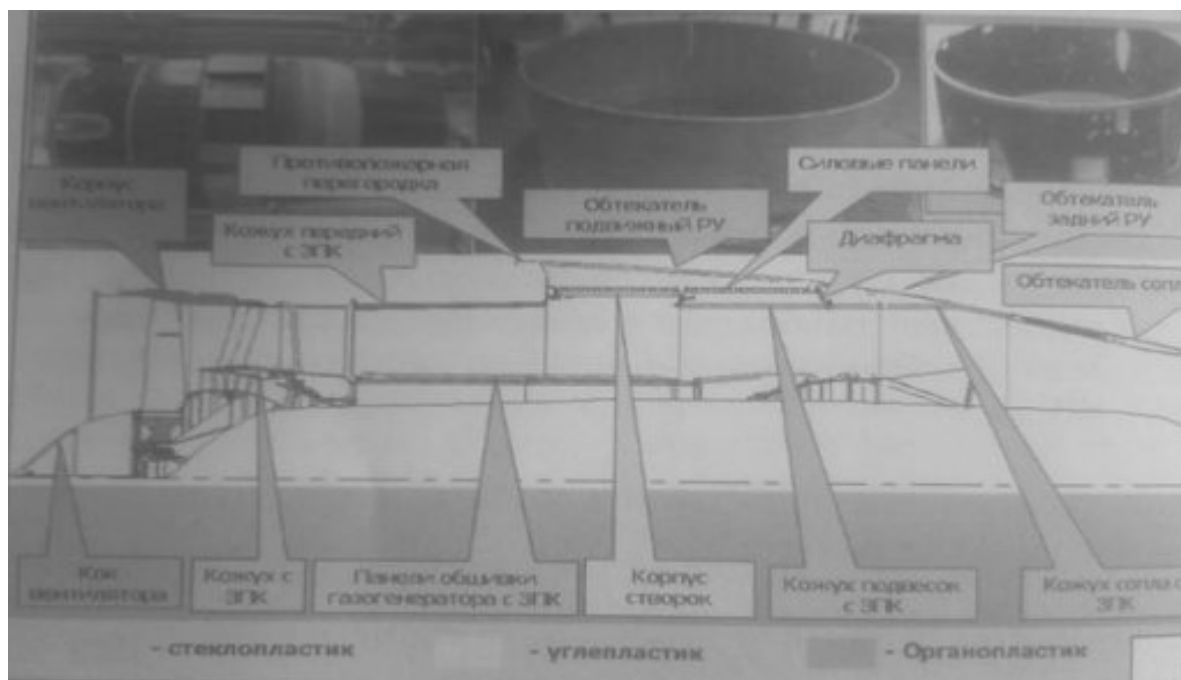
Детали и агрегаты из КМ в конструкции двигателя
